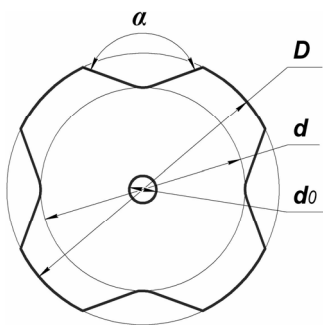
Поперечний переріз чотирипроменевої заготовки
